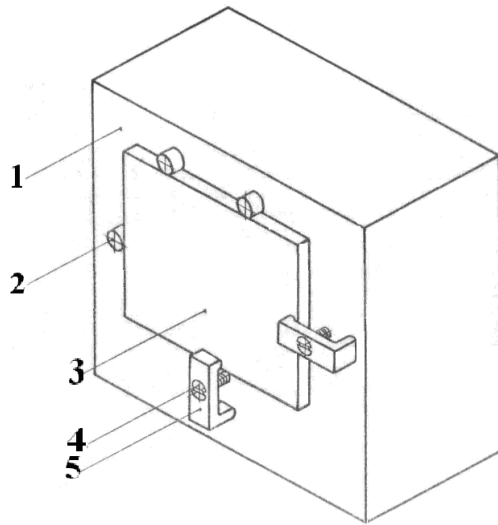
Схема закріплення заготовки на розмічальному пристосуванні (розмічальний ящик): 1 - ящик розміток; 2 - настановний штифт; 3 – Заготовка; 4 – гвинт; 5 - притискна планка
